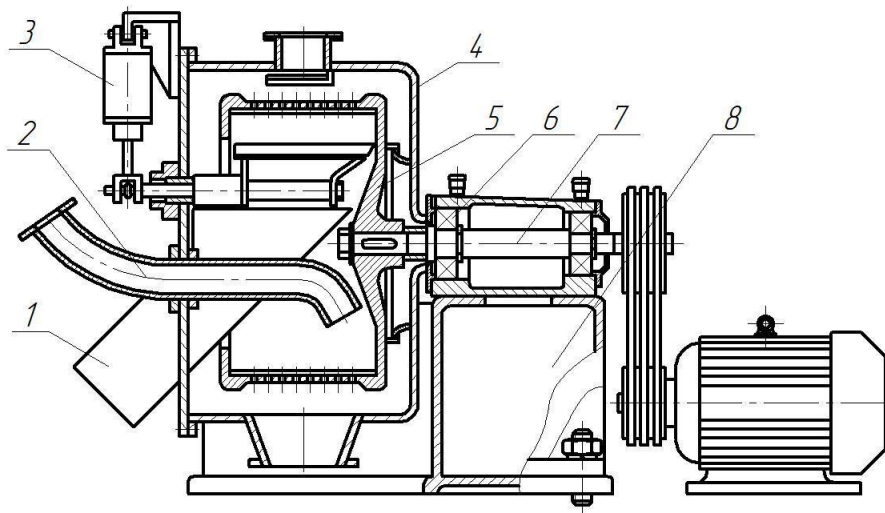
Схема центрифуги типу ФГН: 1 – розвантажувальний жолоб; 2 – живильна труба; 3 – механізм среза осадка; 4 – кожух; 5 – ротор; 6 – підшипники кочення; 7 – вал ротора; 8 – станина
